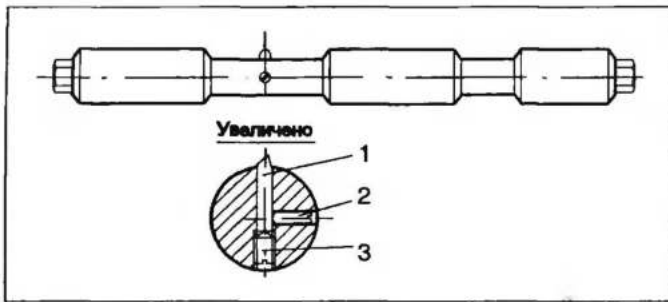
Борштанга (скалка) для ручной расточки поврежденной опоры:
